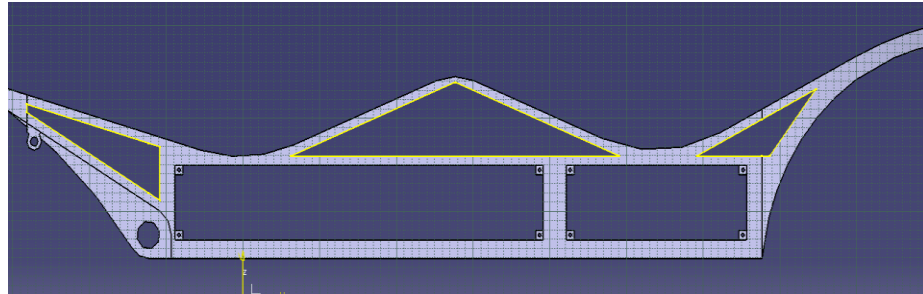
, Secciones proyectadas para hacer los "Pads"
